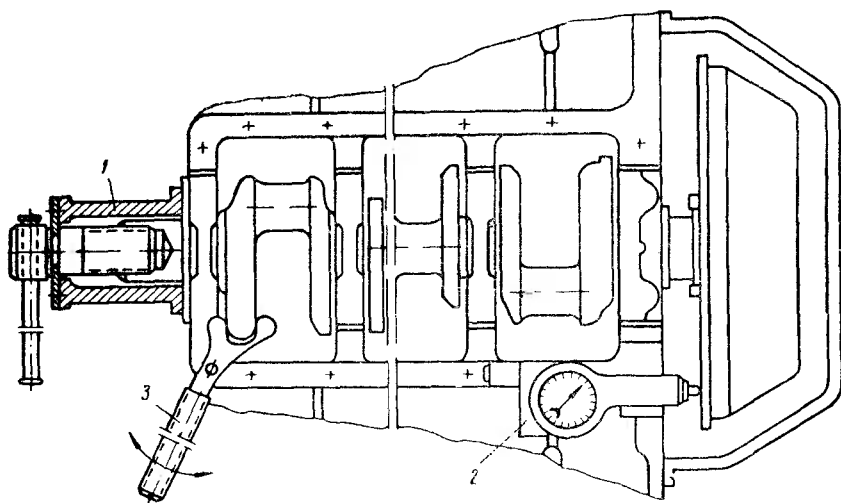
Схема проверки осевого люфта коленчатого вала у двигателя 3МЗ-53: 1 — приспособление для выравнивания торцов крышки первого коренного подшипника и блока; 2 — приспособление для измерения люфта; 3 — рычаг
